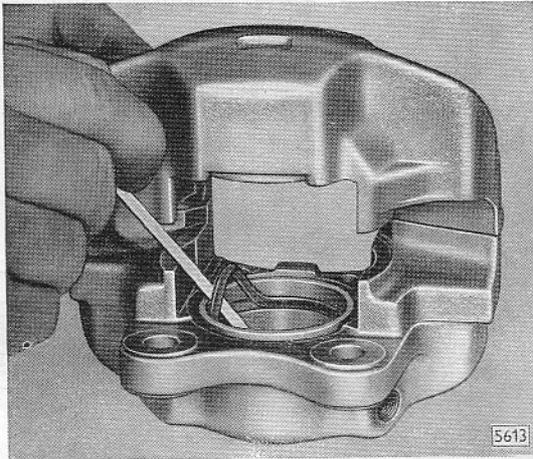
Gummidichtring aus Nut im Zylinder des Deckelgehäuses herauszwingen
